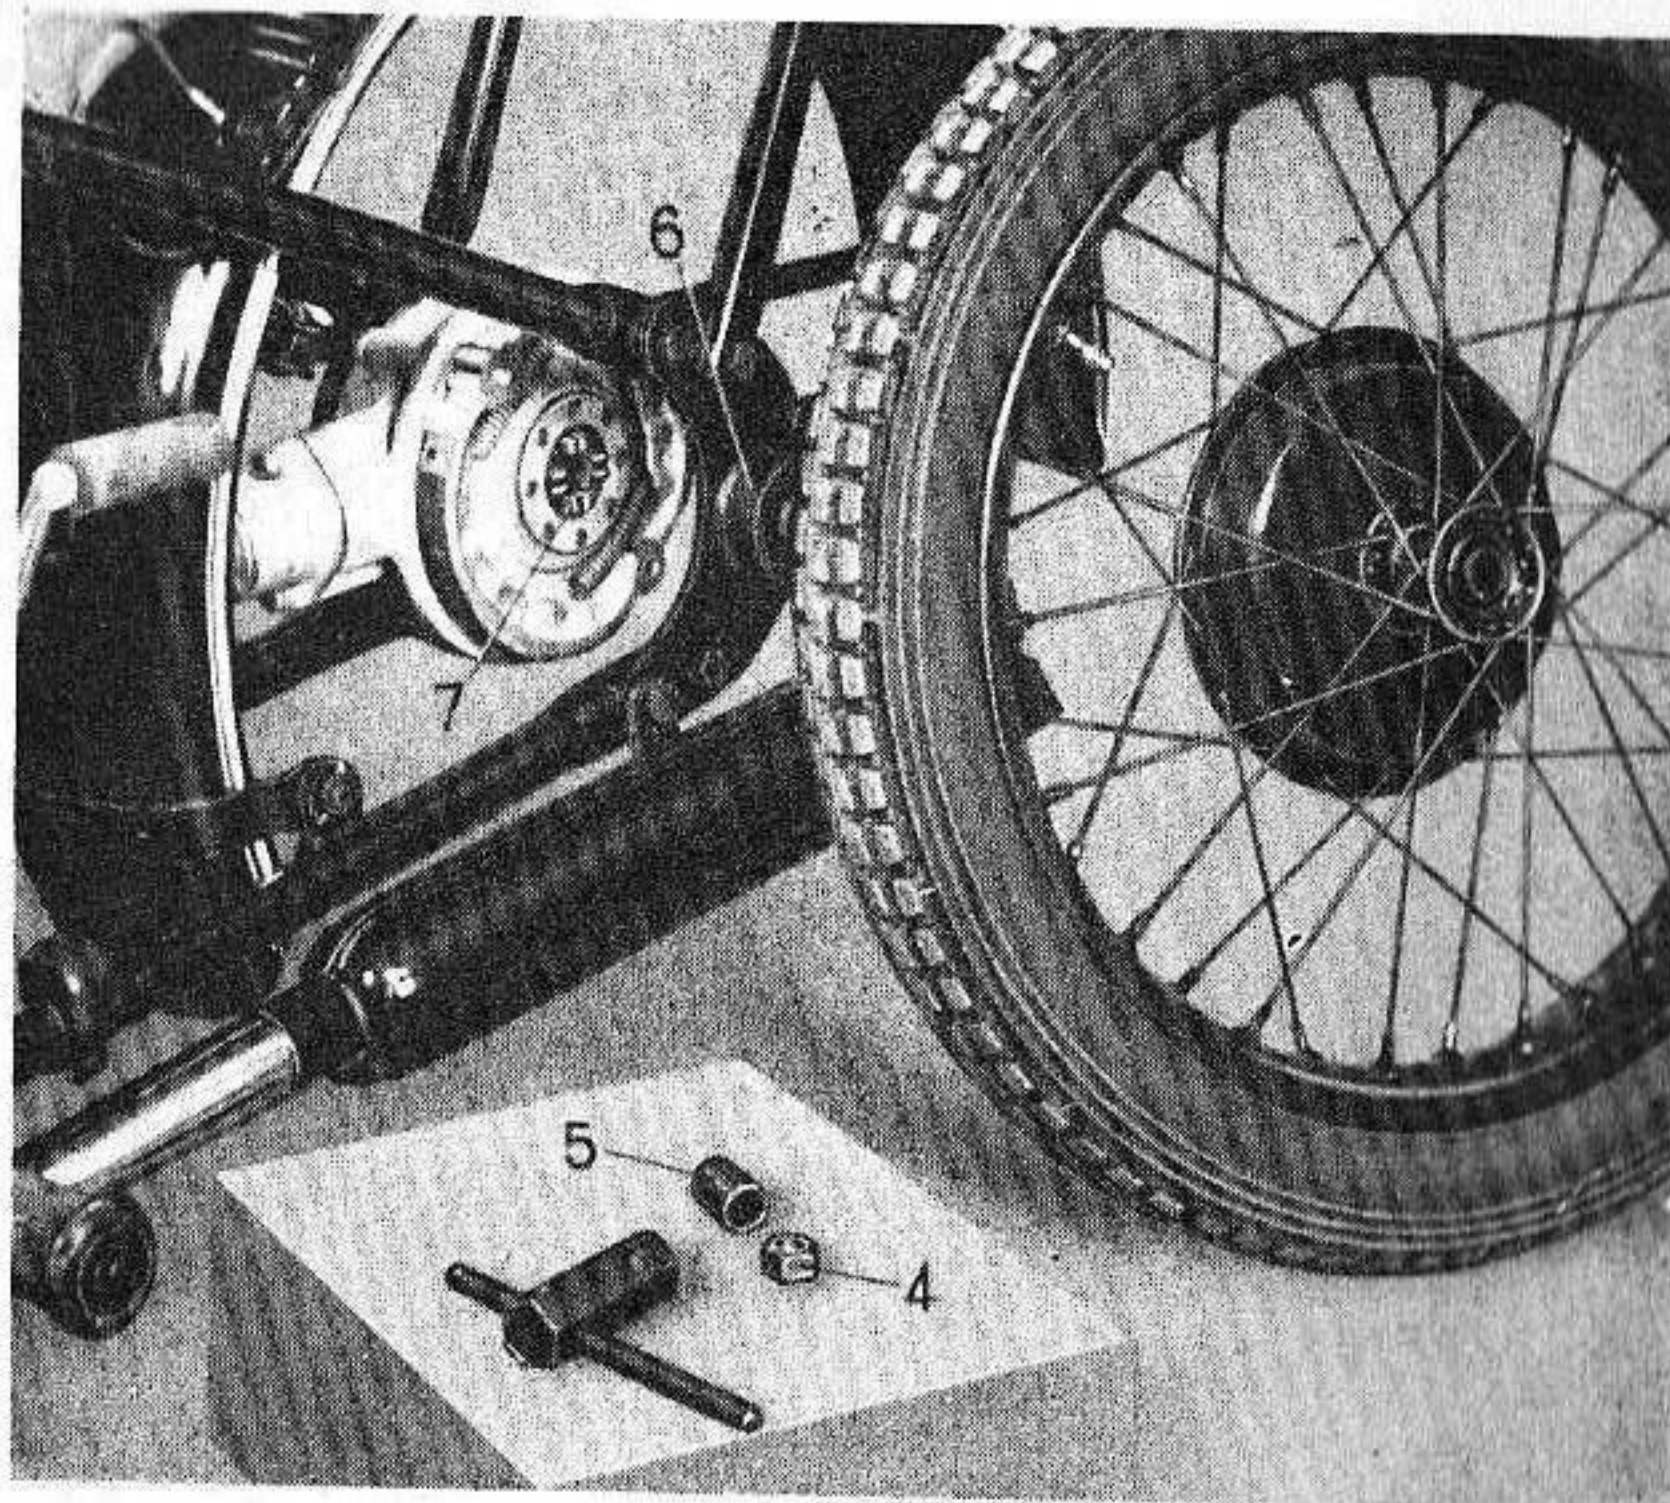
Ausbau des Hinterrades: Auspuffseite
